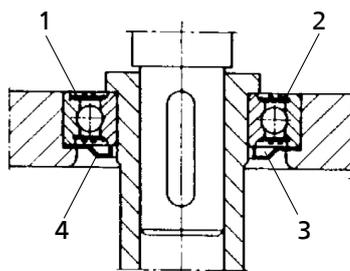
Радиальные шарикоподшипники (опорный подшипник)
